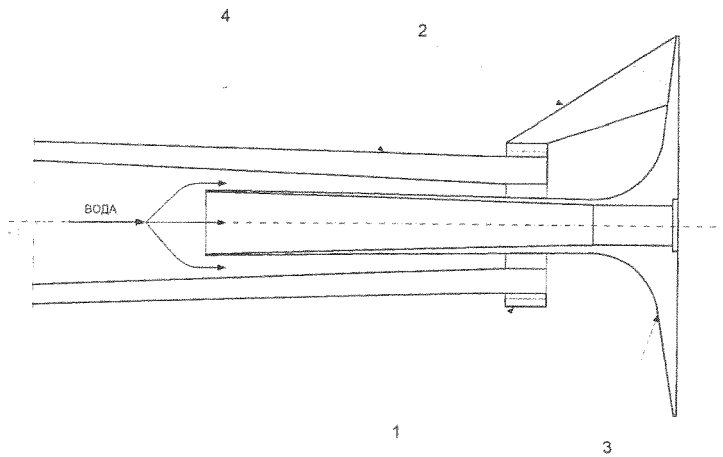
Робота фігурної насадки для ручного пожежного ствола марки РС-70
